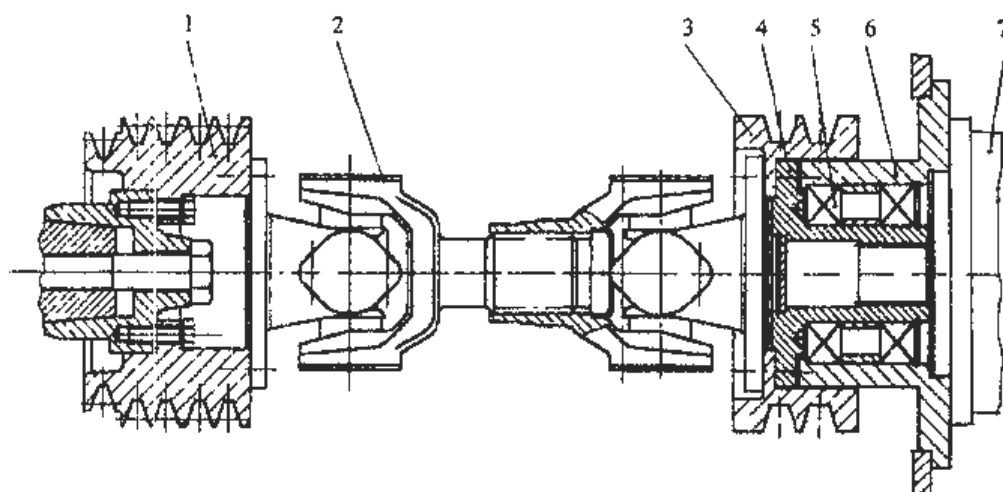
Привод карданный для двигателя ЯМЗ-236ДК9: 1 – шкив; 2 – кардан КИС-0106860; 3 – шкив; 4 – ступица; 5 – подшипник; 6 – корпус; 7 – насос гидростатической трансмиссии
